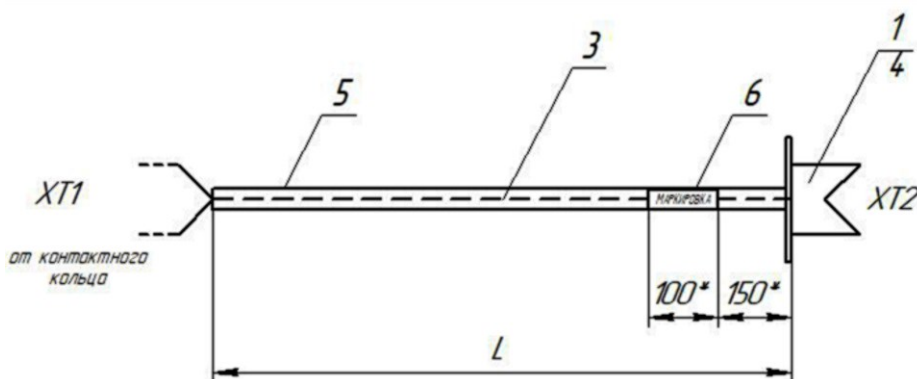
Схематичный внешний вид кабеля Eth.УАПП
